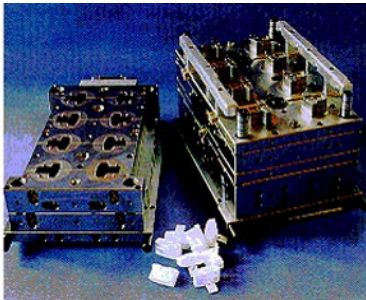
mfZ) Spritzgusswerkzeug mit verschiedenen Kavitäten
